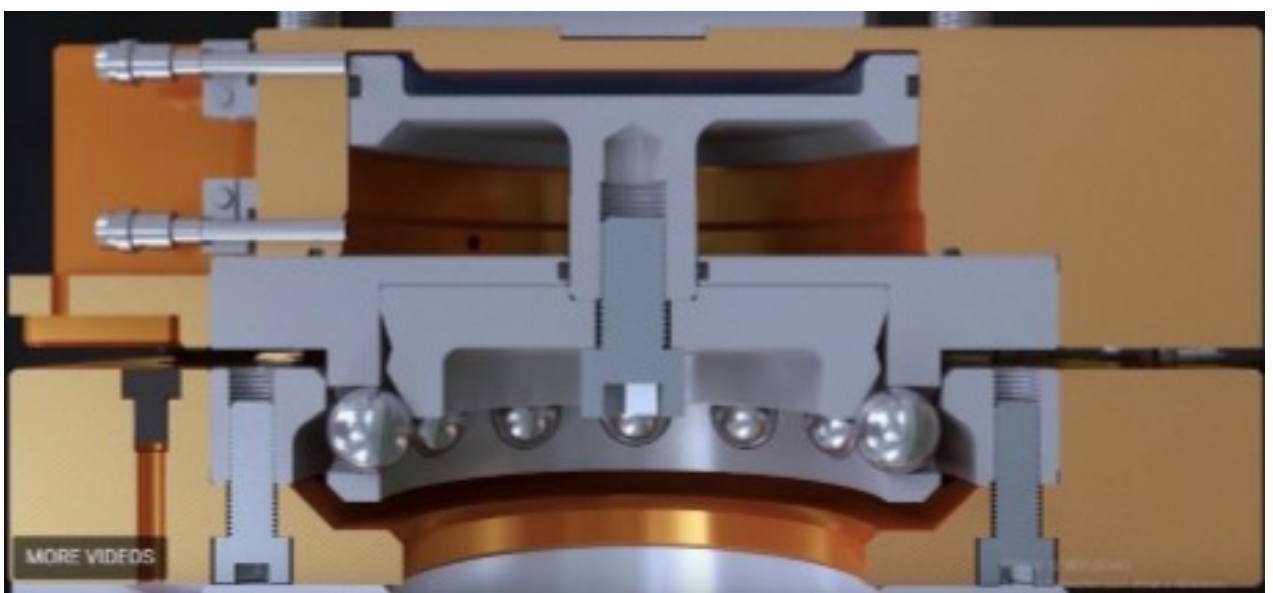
Пристрій для зміни інструменту перед зеднанням
